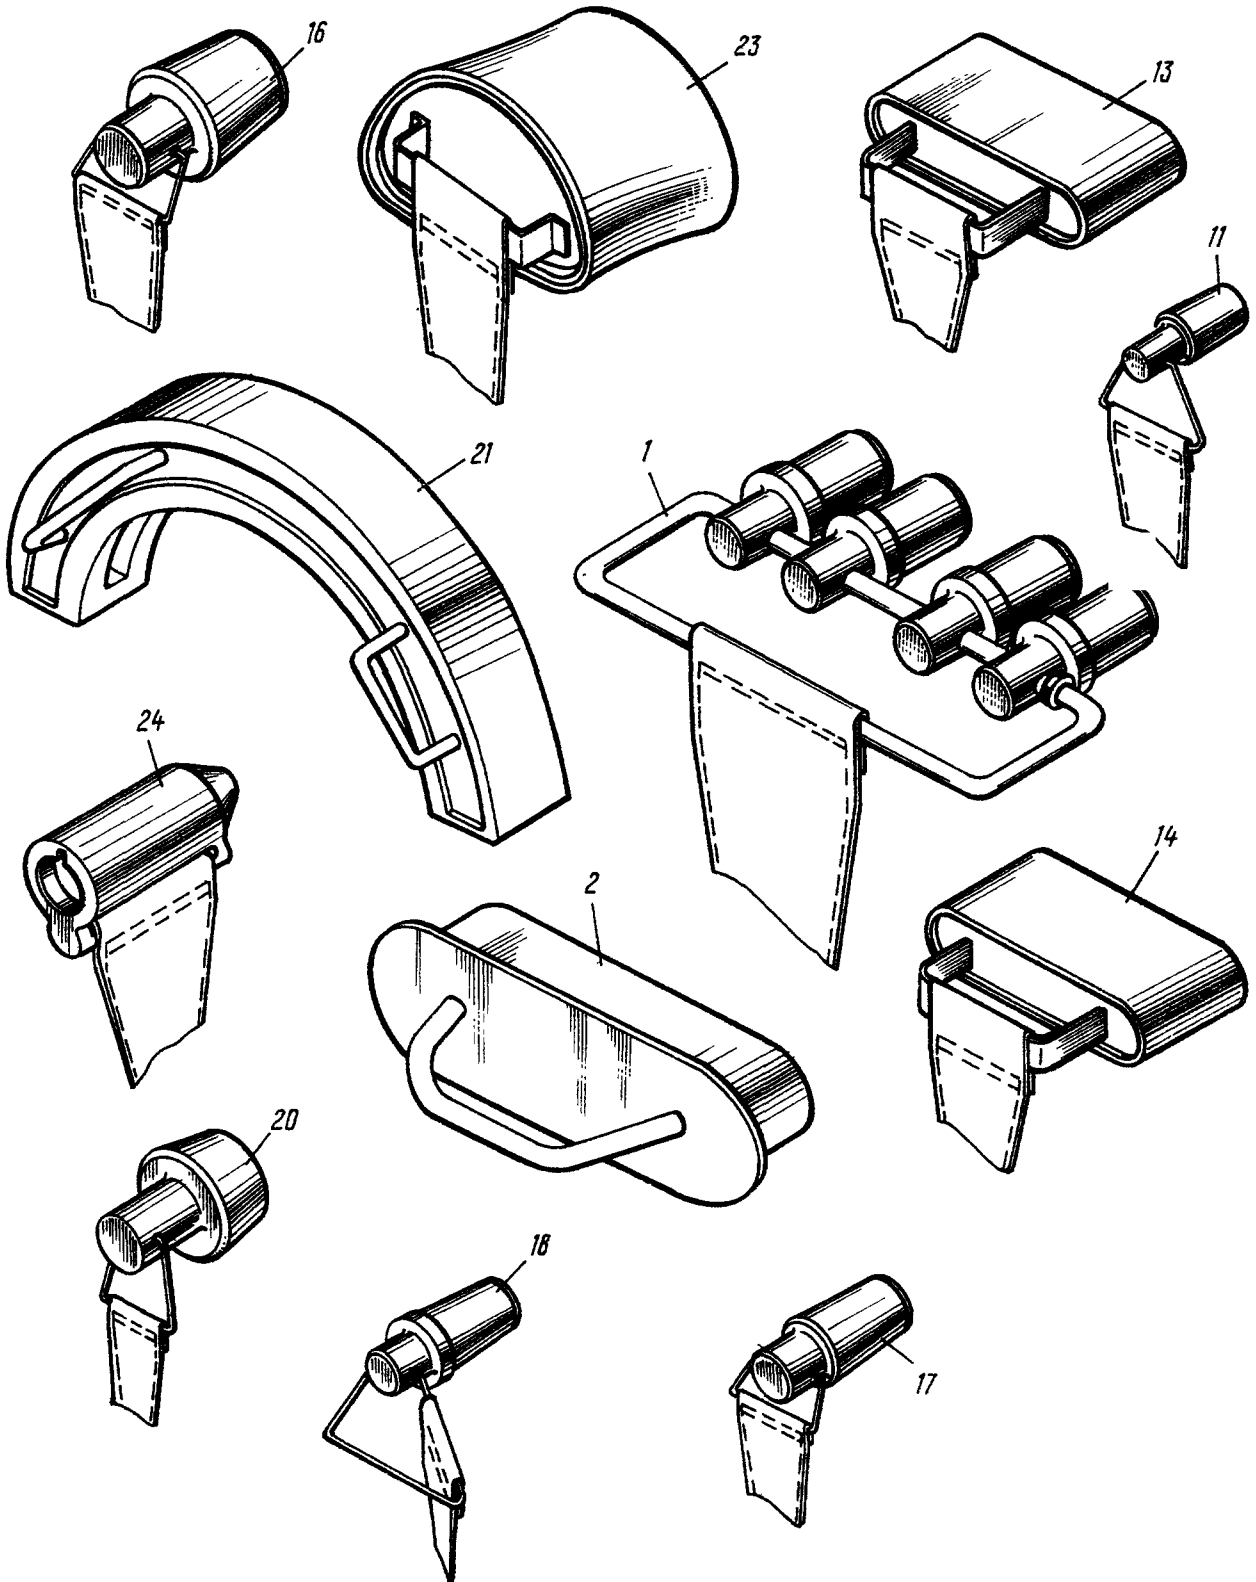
УСТАНОВКА ЗАПЛИВК (ЛИСТ 3)
